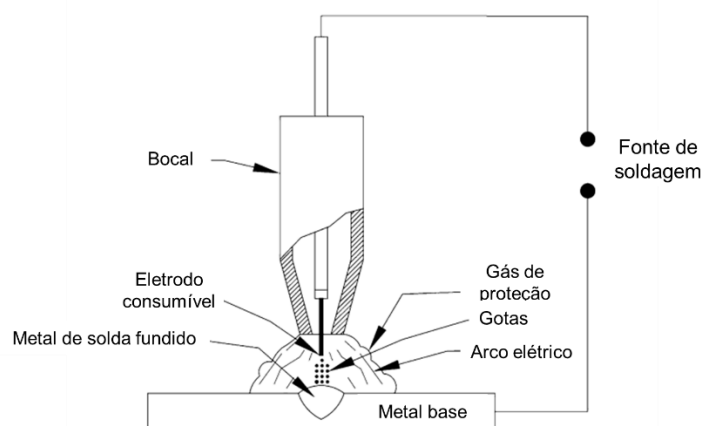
Circuito de soldagem GMAW (Adaptado de PAL; PAL, 2011)
